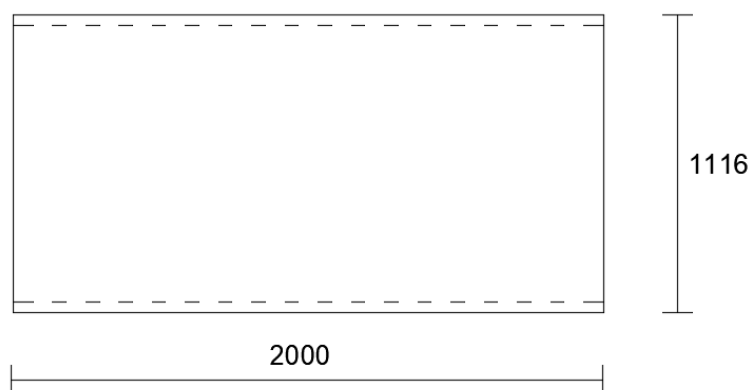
Dimensiones de la carcasa cilíndrica exterior del depósito PHV-003.
